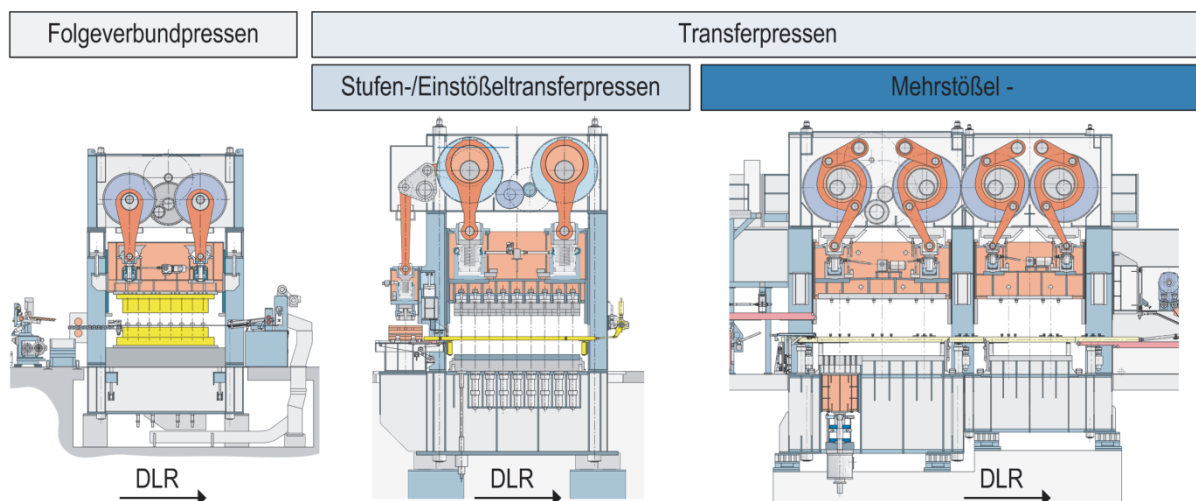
Pressmaschinen für Folgeverbund- und Transferwerkzeuge (in Anlehnung an SCHULER [91])
